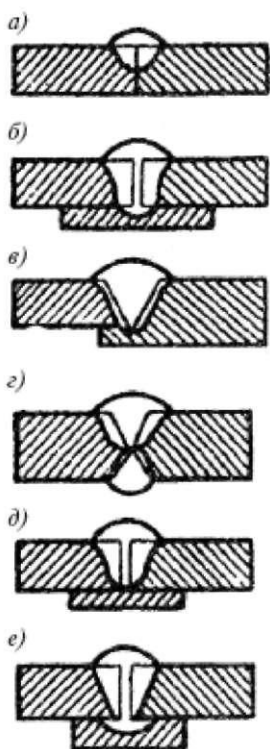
Способы односторонней автоматической сварки под флюсом: *а* - без разделки кромок с неполным проваром; *б* - сварка на остающейся стальной подкладке; *в* - сварка в замок; *г* - сварка с предварительной подваркой; *д* - сварка на медной подкладке; *е* - сварка на медно-флюсовой подкладке
